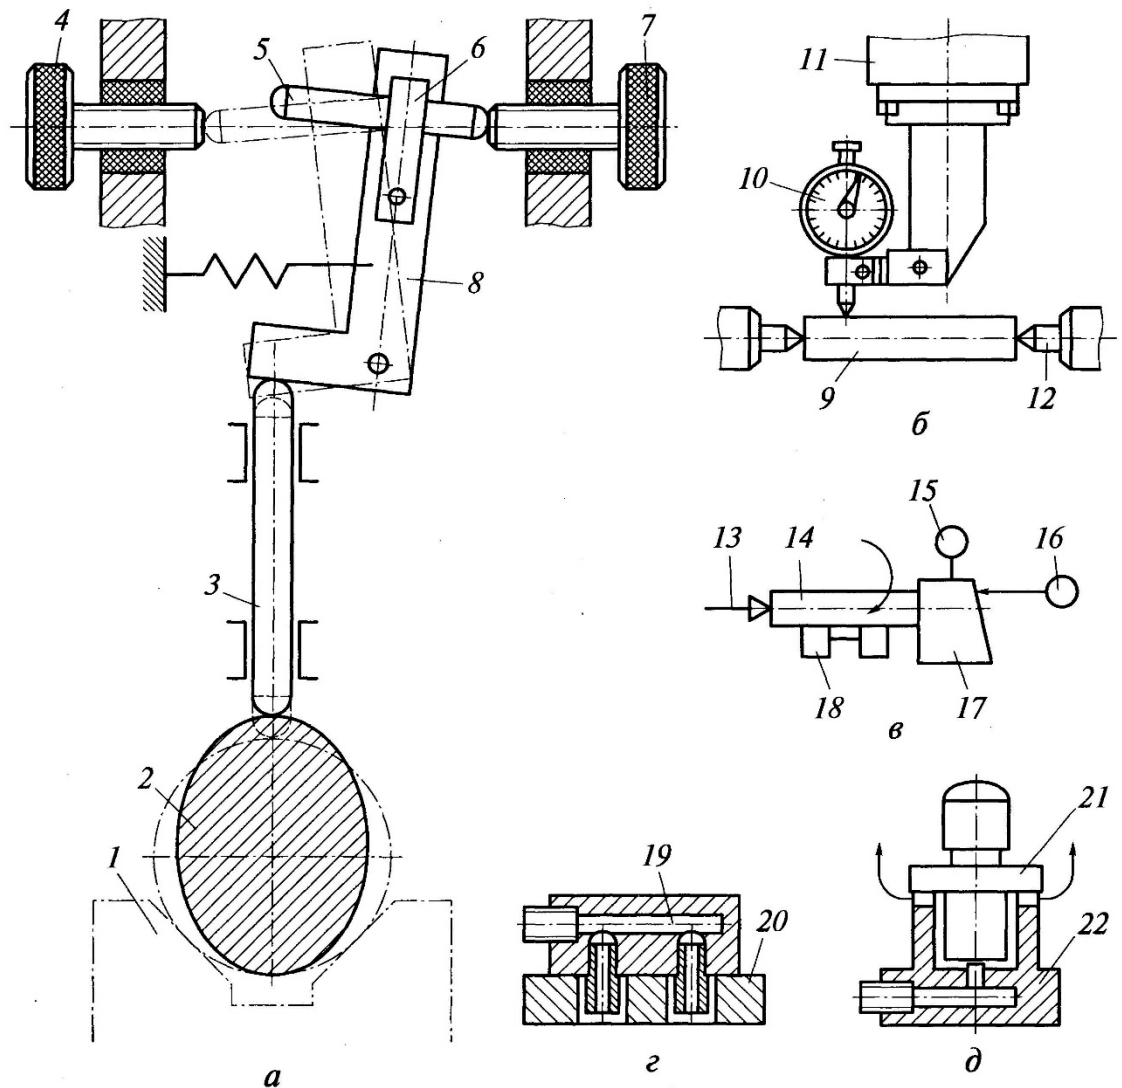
Схеми контролю відхилень форми деталі:
